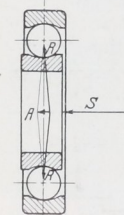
Wirkung axialer Belastung auf Querlager.
